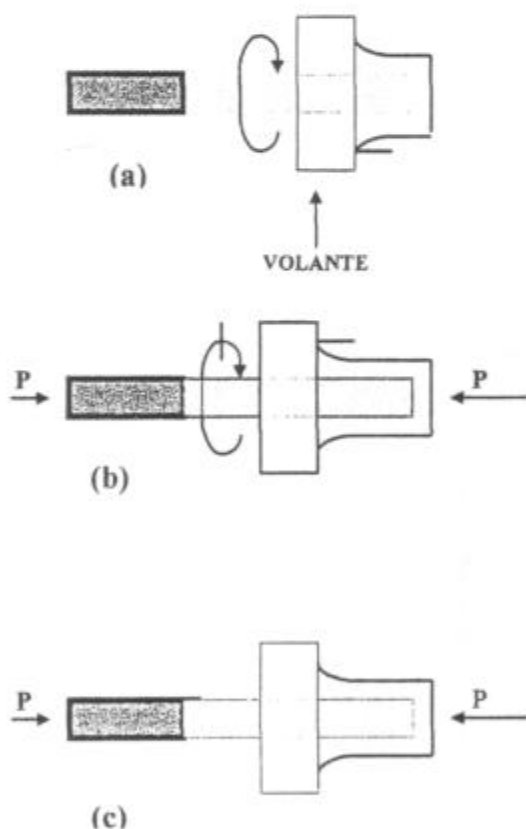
Operaciones en la soldadura por inercia.
